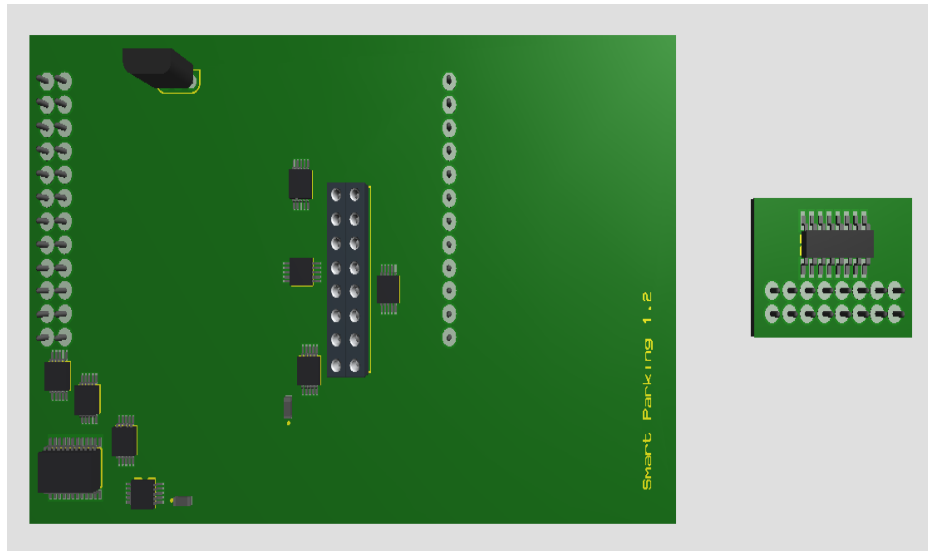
Vista Superior de placa Smart Parking y sensor magnético.
